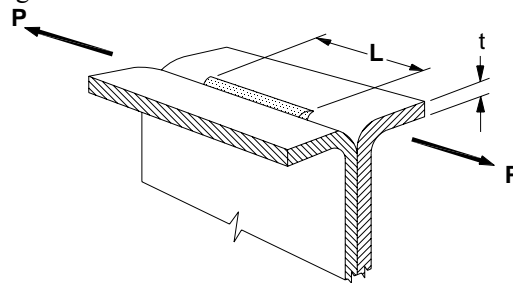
Cortante en soldadura de ranura biselada – V
